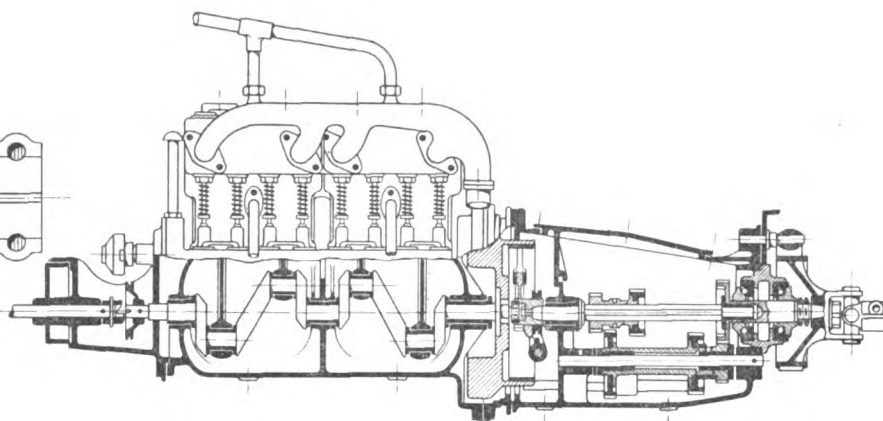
Motor und Getriebe der neuen Pariser Automobildroschken.
